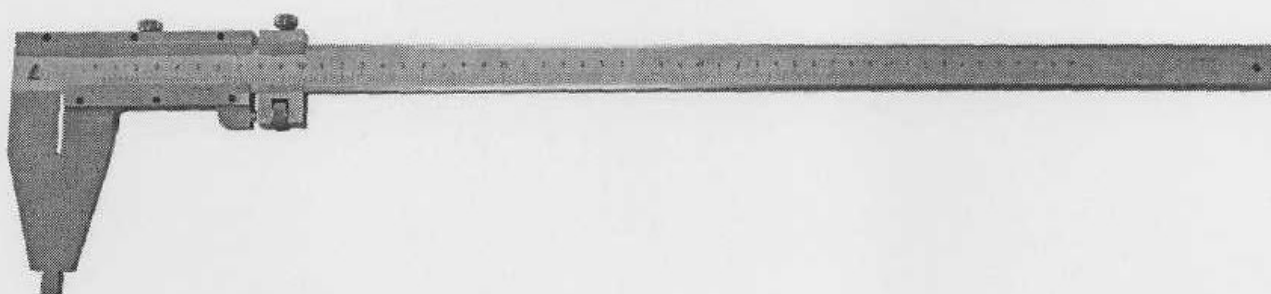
Внешний вид штангенциркулей ШЦ-III
